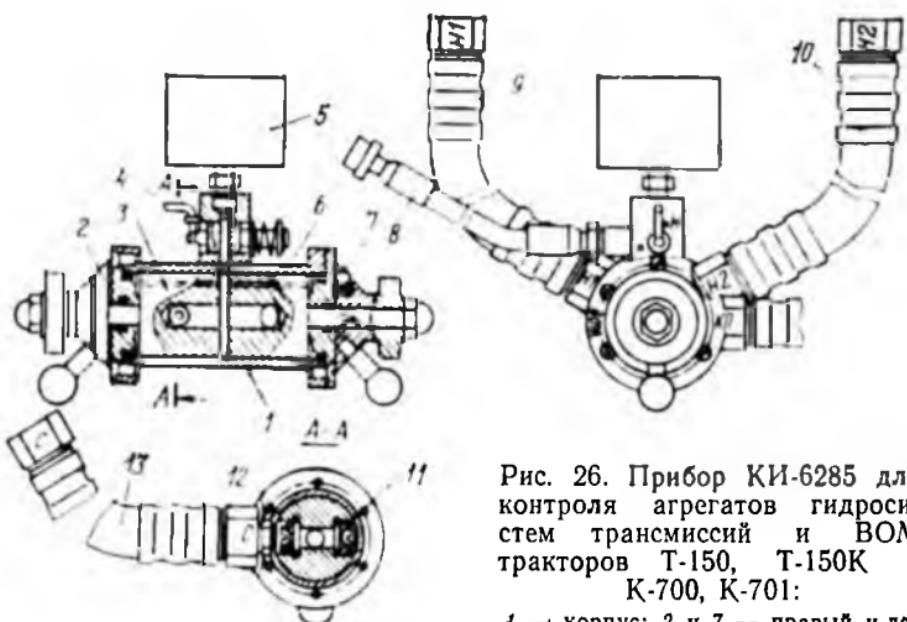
Прибор КИ-6285 для контроля агрегатов гидросистем трансмиссий и ВОМ тракторов Т-150, Т-150К и К-700, К-701:
